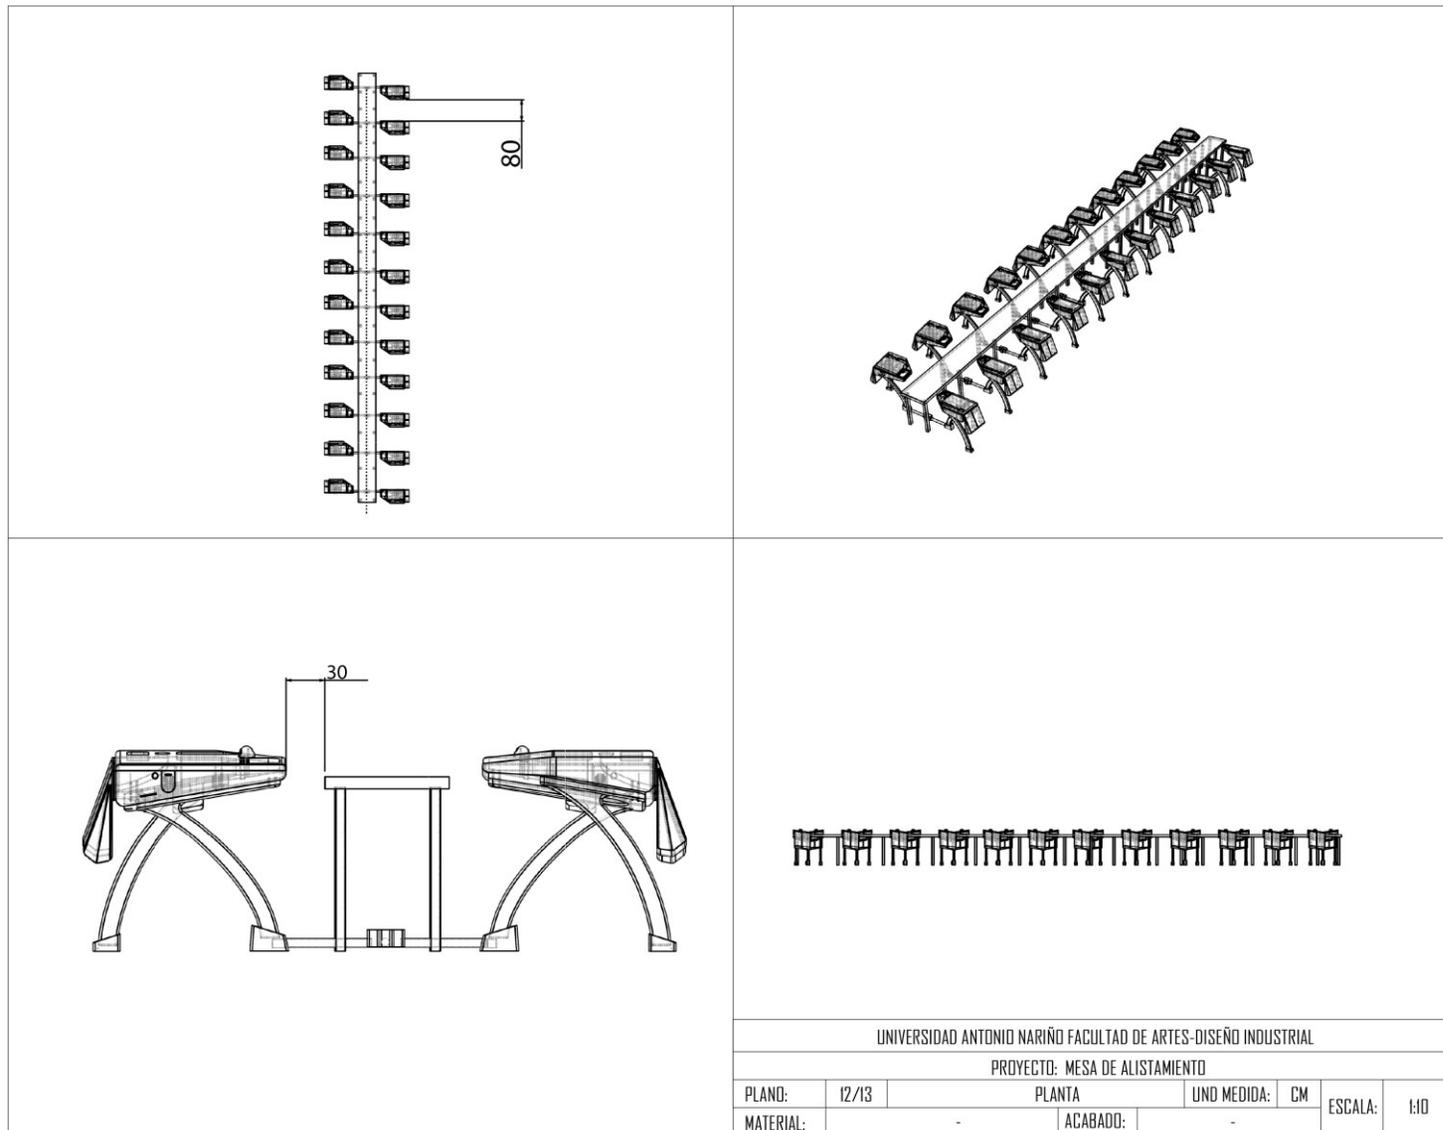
Planos piezas 12 (Elaboración propia, 2020)
